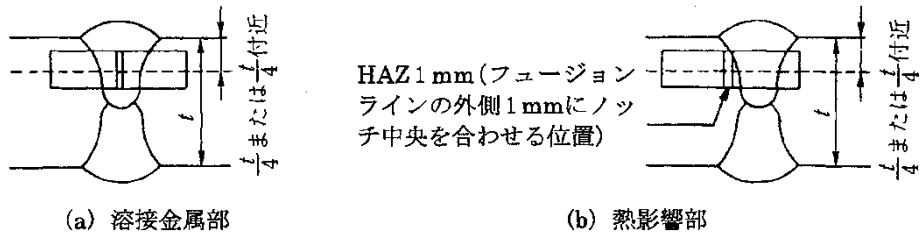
衝撃試験片（開先溶接試験片の採取位置）
